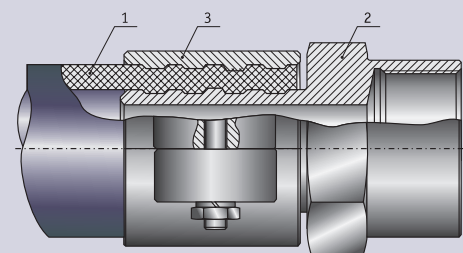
Схема соединения с обжимным хомутом: 1 — труба из сшитого полиэтилена; 2 — штуцер с монтажным шестигранником и резьбовым хвостовиком; 3 — обжимной хомут со стяжным болтом и гайкой
